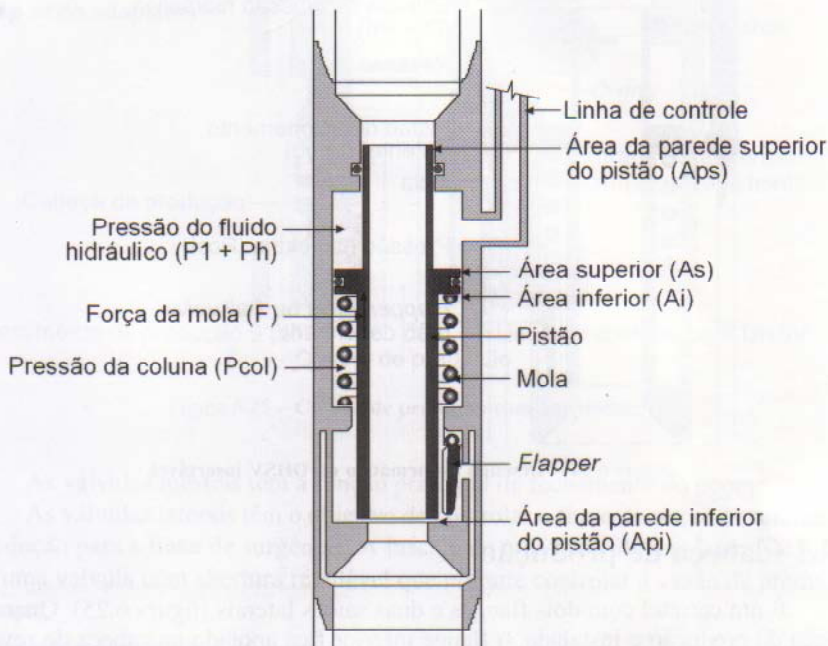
Desenho esquemático da DHSV tubing mounted.
